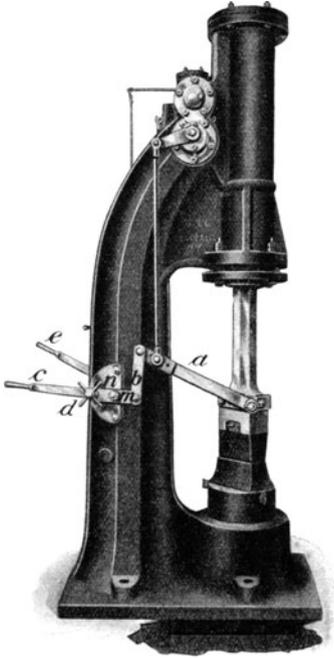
Dampfhämmer der Buffalo Foundry & Machine Co. in Buffalo.
